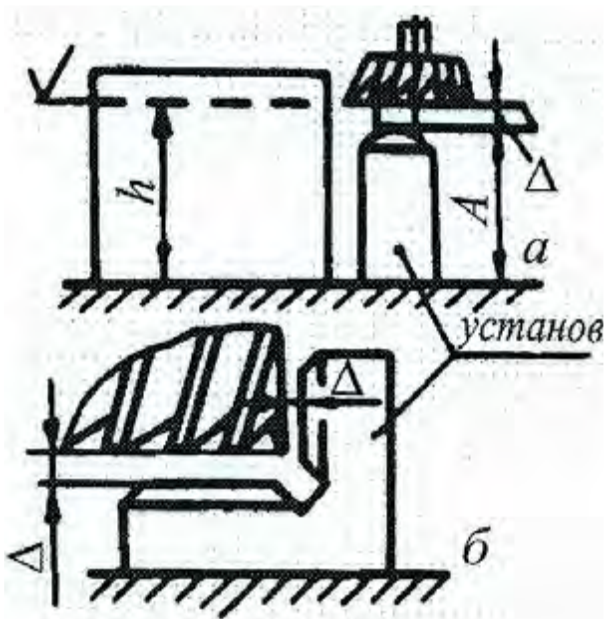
Висотний (а) і кутовий (б) установи для фрезерних пристроїв
